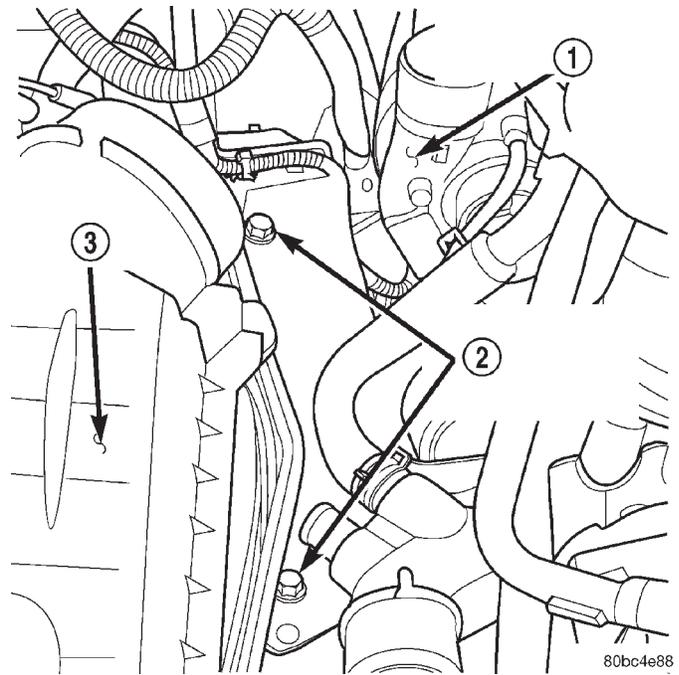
Schrauben des Sockels/Motoraufhängung—
